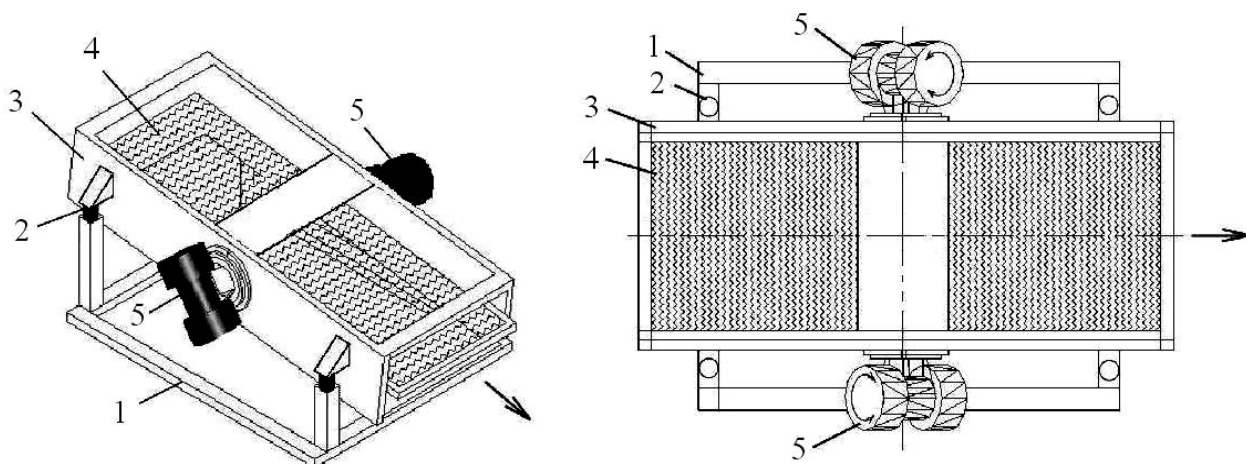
Конструкция грохота с пространственными колебаниями короба: 1 – рама; 2 – амортизаторы; 3 – короб; 4 – просеивающая поверхность; 5 – вибропривод.
